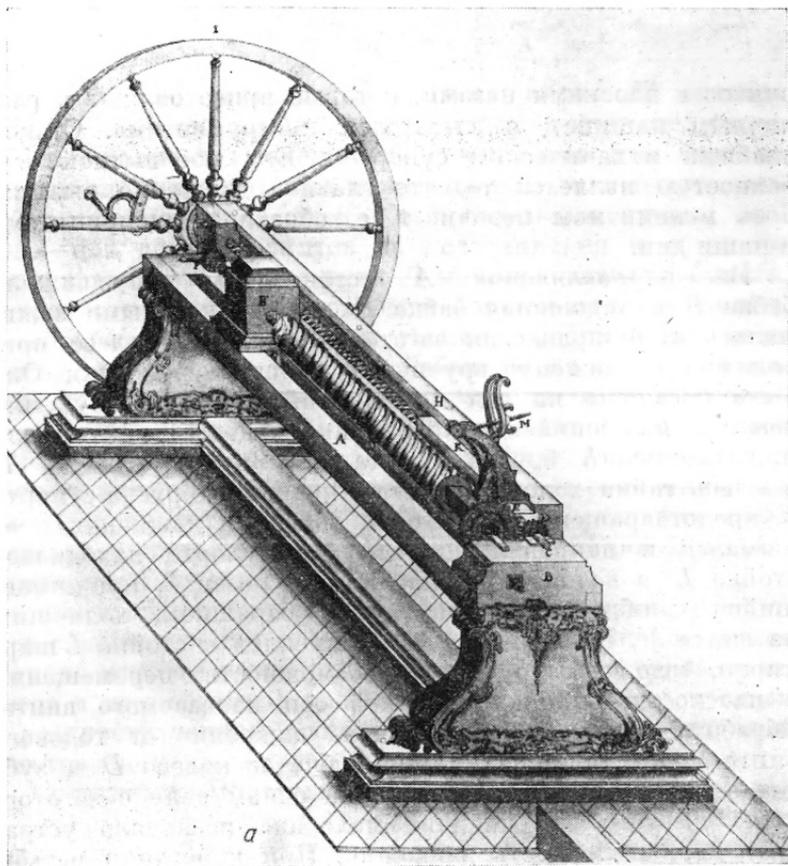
Токарно-винторезный станок для изготовления крупных многозаходных винтов с механизированным суппортом и набором сменных зубчатых колес. 1738 г. («Театрум махинарум»).
